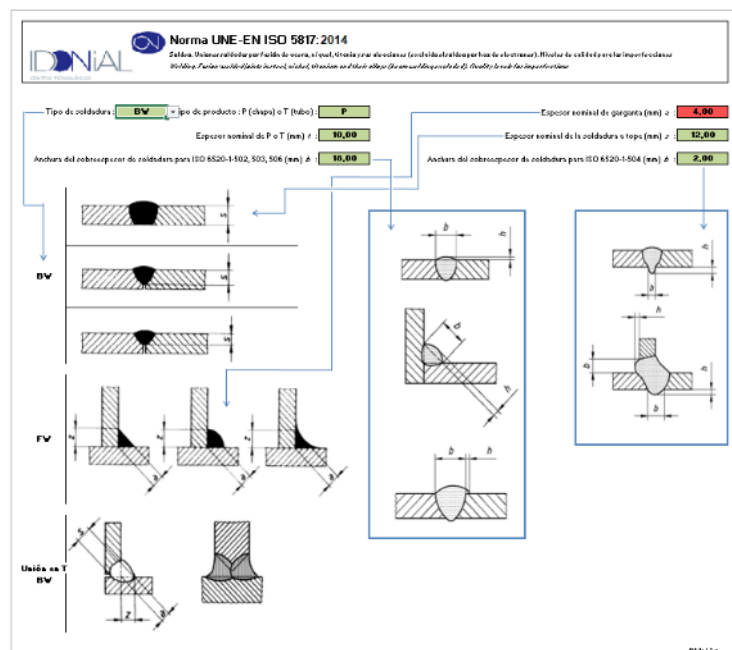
Definición de espesores y tipo de cupón de soldadura.
